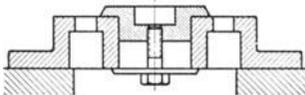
Einlage für einen innen vorgearbeiteten Zuschnitt.
